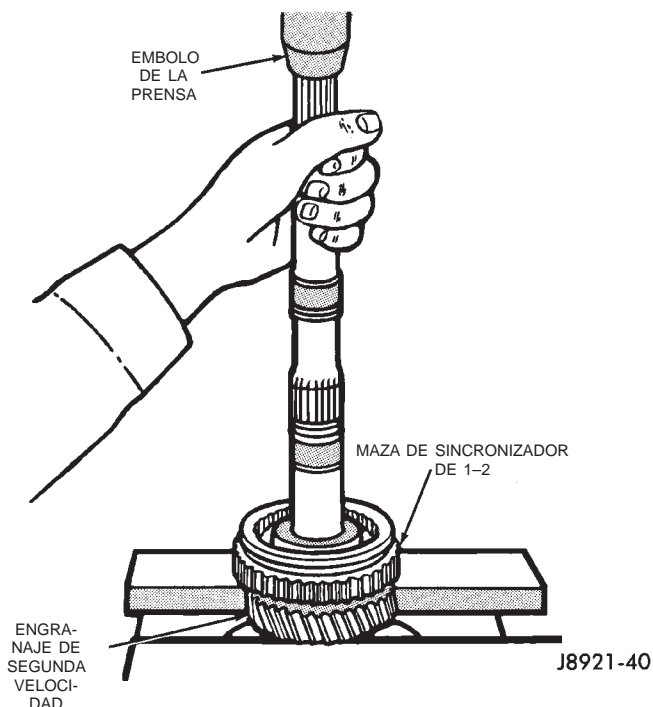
Desmontaje de engranaje de segunda velocidad, engranaje de marcha atrás y el sincronizador de 1-2
